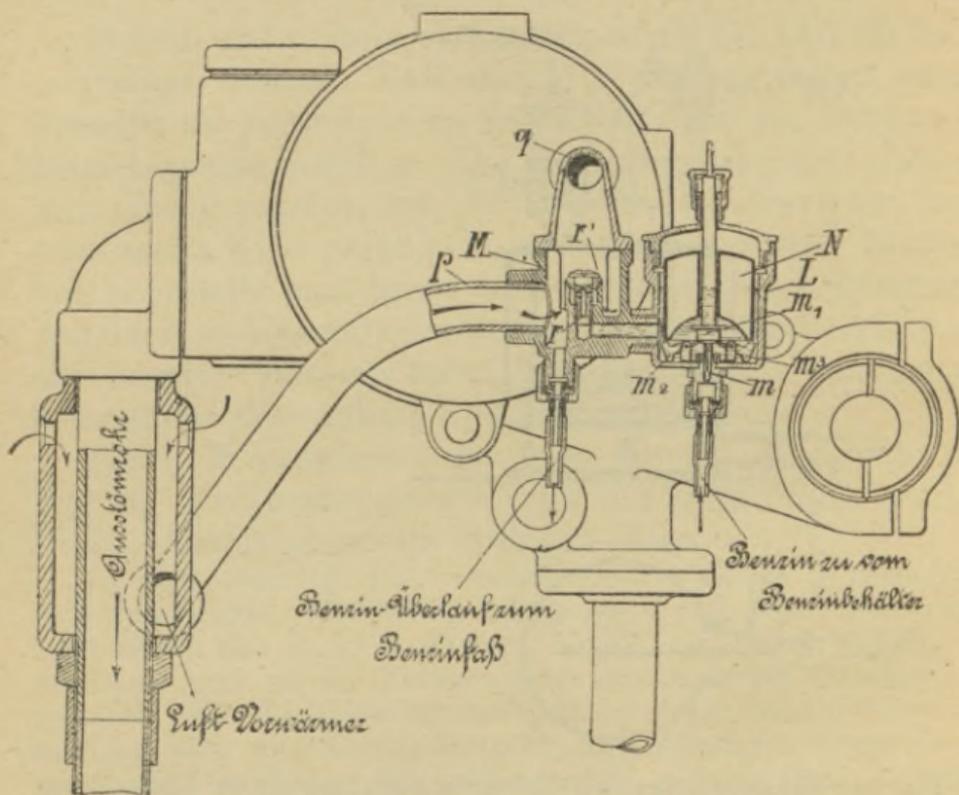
Benzingaserzeuger (Einspritzkarburator) der Gasmotorenfabrik Deutz.
